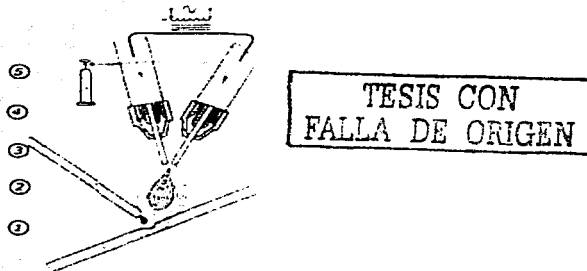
Soldadura atómica con atmósfera de H_2 (Método Langmuir) [1]
